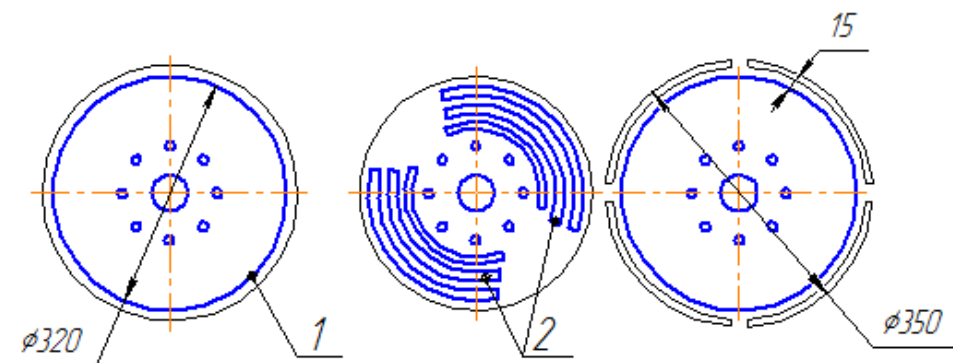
Принцип відновлення дисків 1 - базова деталь, 2 – шматочки для відновлення
